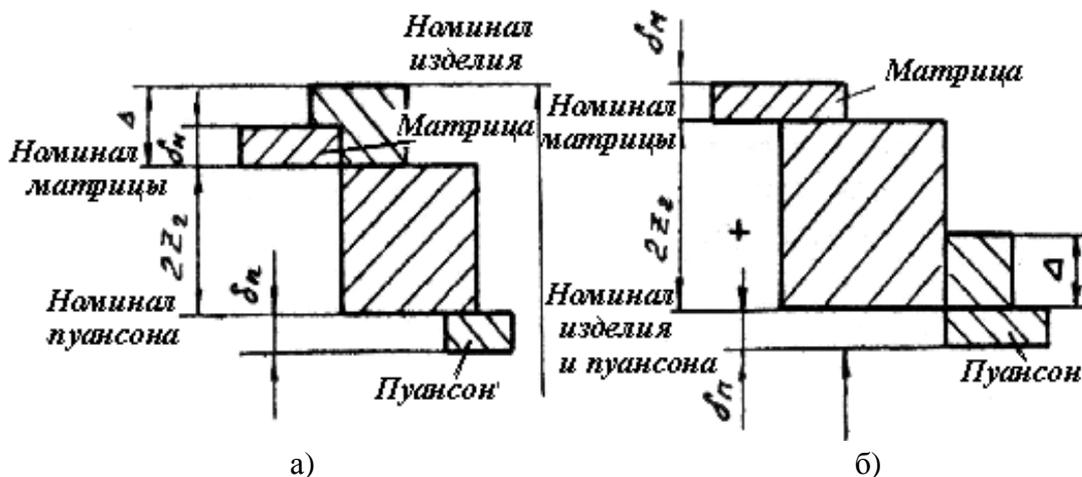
Схемы расположения допусков на исполнительные (рабочие) размеры матрицы и пуансона штампа для гибки скобы: а – по наружному, б – по внутреннему размеру
